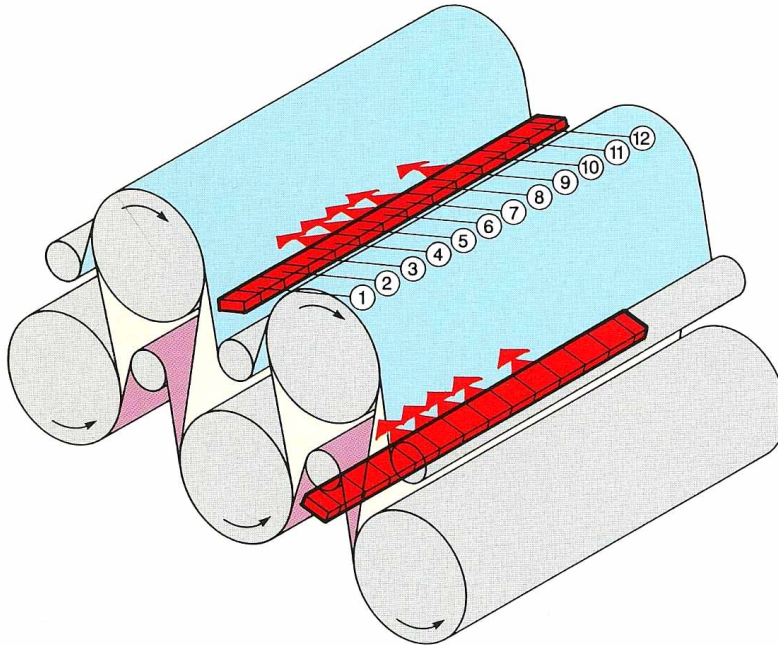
Correction du profil en travers par soufflage sélectif d'air.
